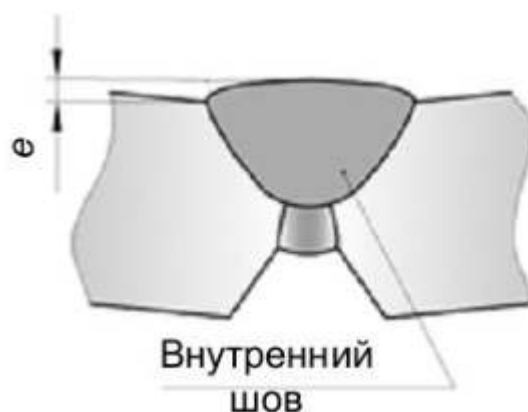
Внутренний сварной шов в сечении
